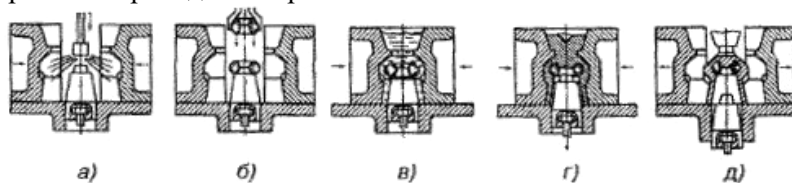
Последовательность изготовления отливки в кокиле (стрелки - последовательность направления движения деталей кокиля):
